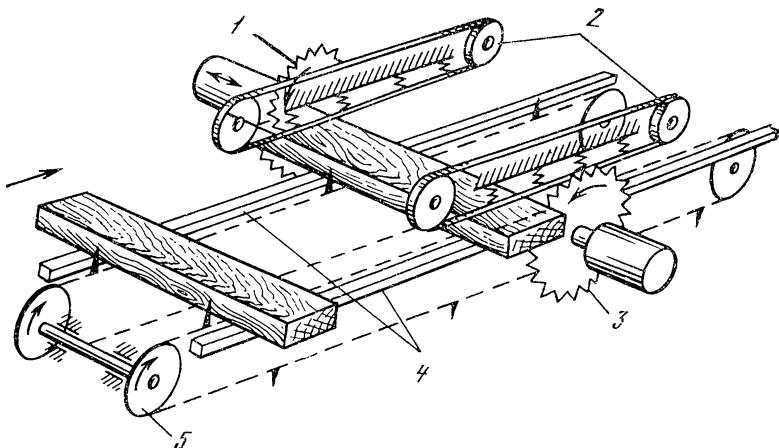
Схема торцевания заготовок на двухпильном концеравнительном станке:
